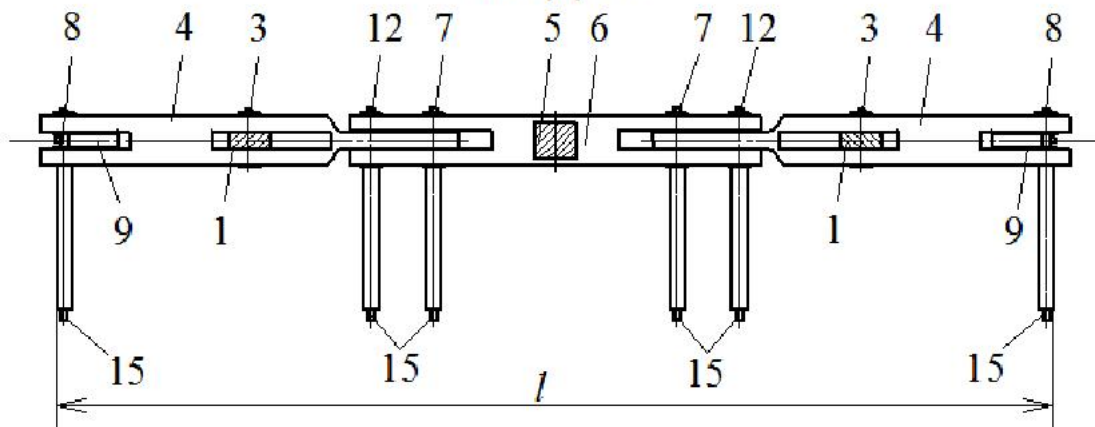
Важільно – шарнірний захоплюючий пристрій
